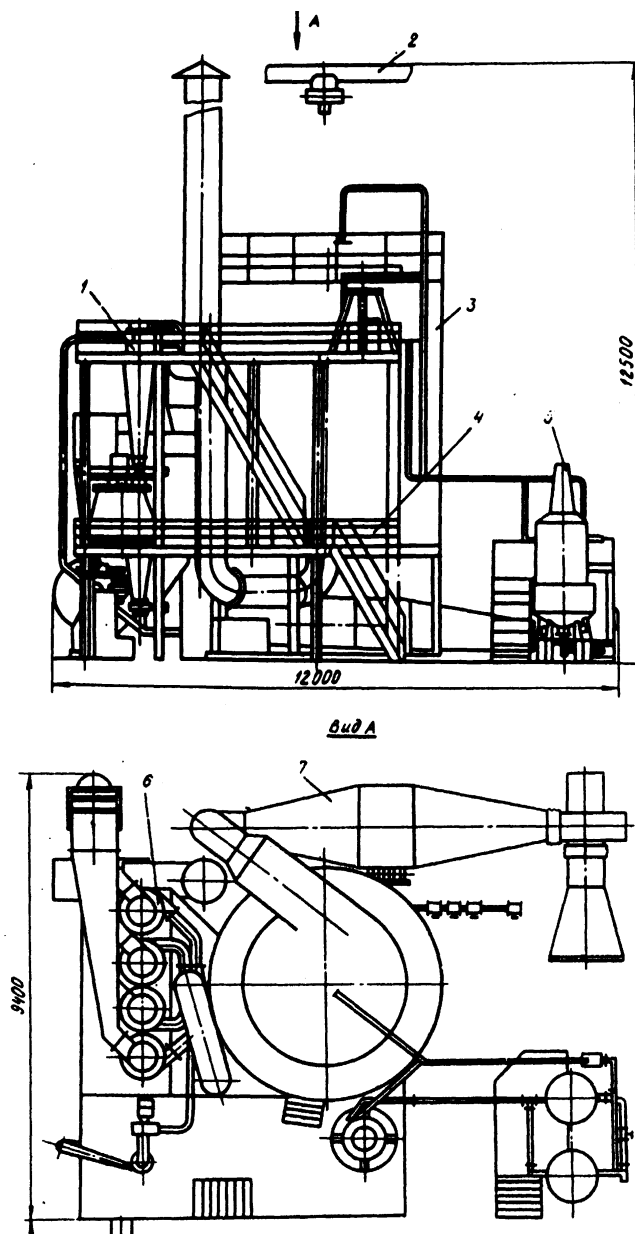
Загальний вид розпилювальної сушильної установки А1-ОРЧ
